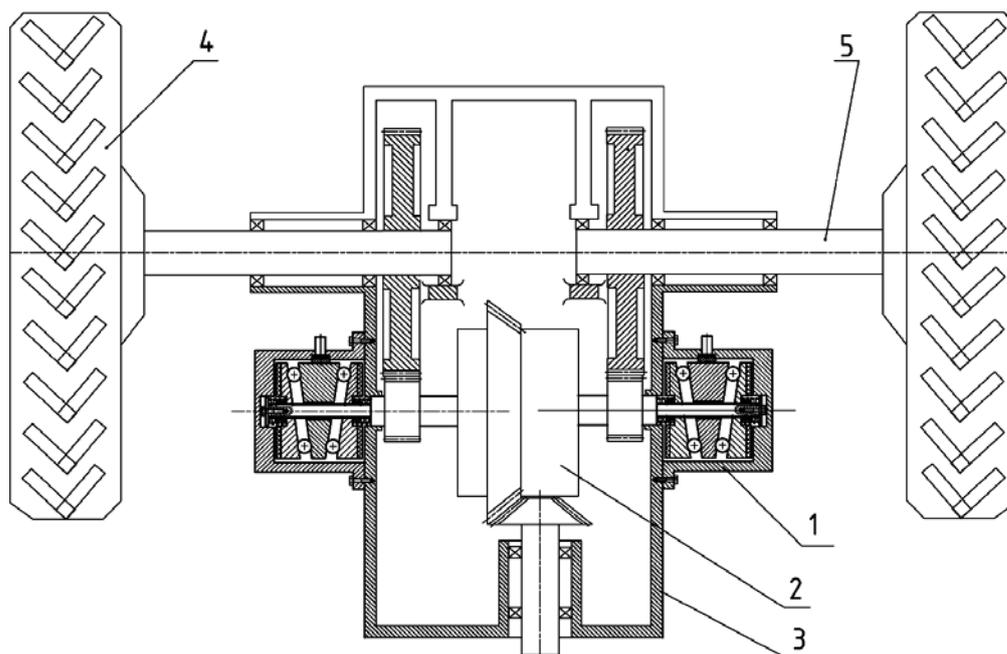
Задний мост трактора с установленными тормозными механизмами: 1 – тормозной механизм; 2 – дифференциал; 3 – корпус заднего моста; 4 – заднее колесо; 5 – полуось
